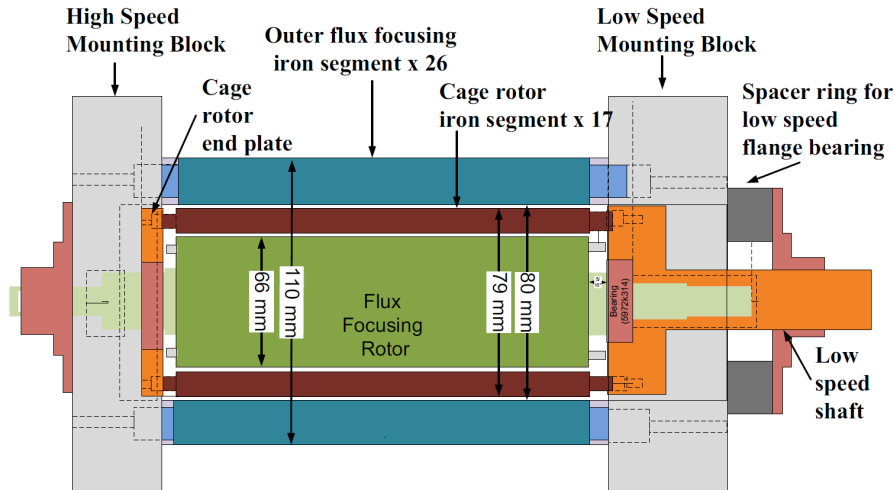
Prototype [34] en assemblage "sandwich"
